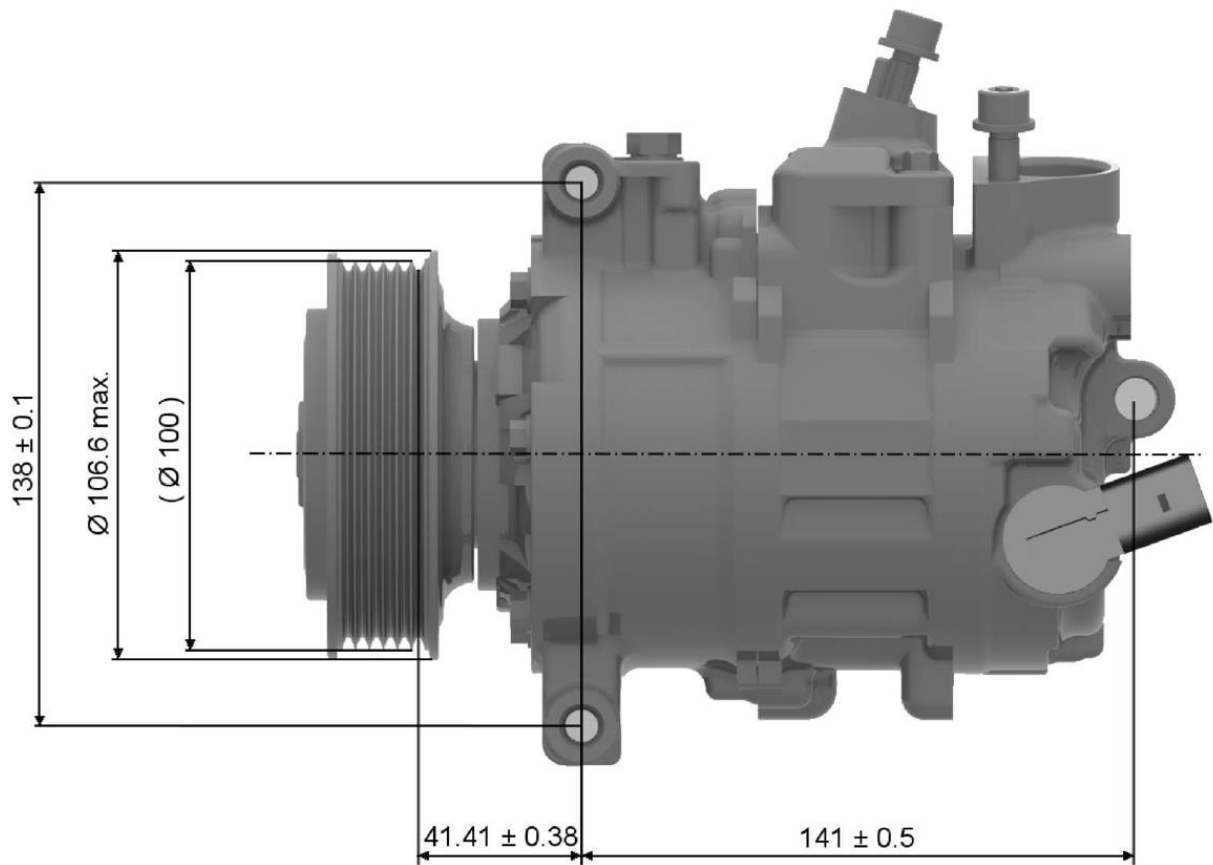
Размеры компрессора климатической установки, диаметр шкива 100 мм, (вид сбоку)
